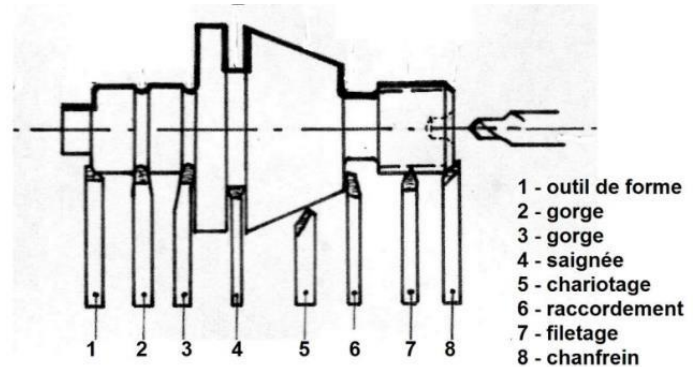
USINAGE EXTERNE SUR TOUR [6]
